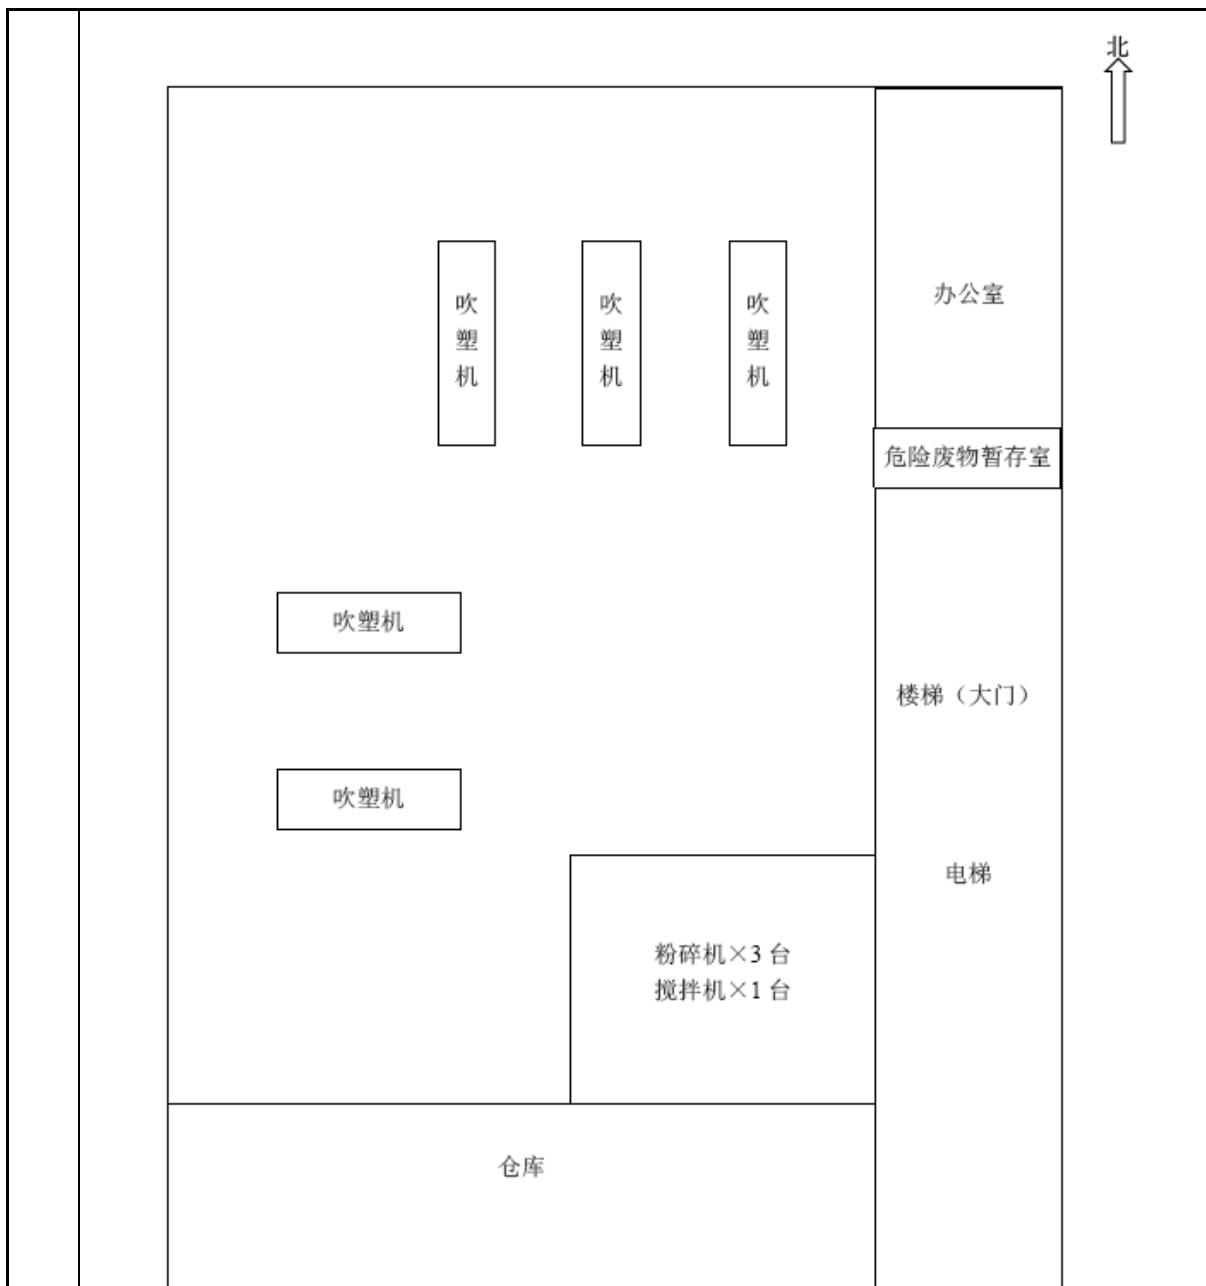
2F 车间平面布置图 (3F~4F 为仓库)
